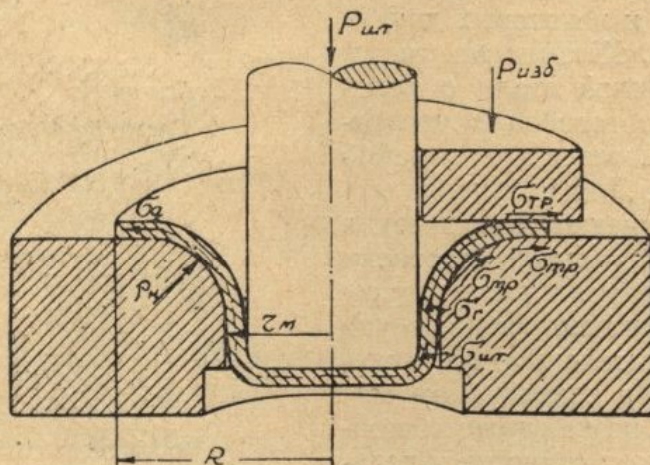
Схема напряженного состояния штампуемой заготовки.
